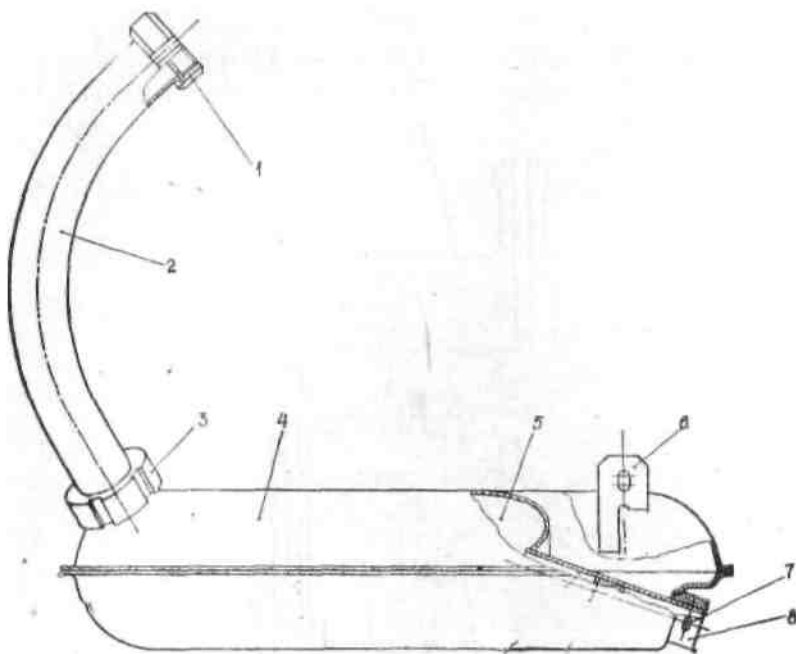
Глушитель: 1—накидная гайка; 2—труба; 3—гайка; 4—корпус глушителя; 5—перегородка; 6—хомут; 7—дросселирующая трубка; 8—выхлопной патрубок.
